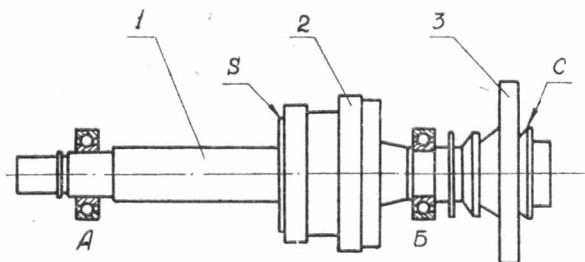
Конструктивная схема ротора: 1 — вал; 2 — крыльчатка насоса; 3 — колесо турбины
